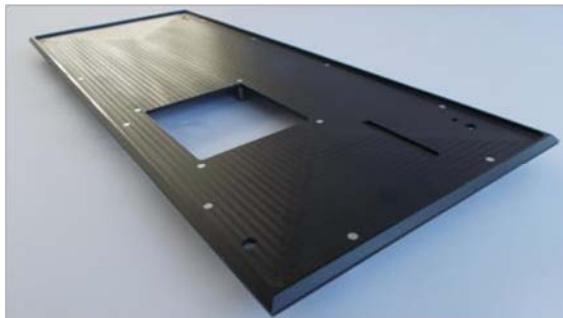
Frontplatte mit flächiger Ausfräsung für eine Glasplatte
